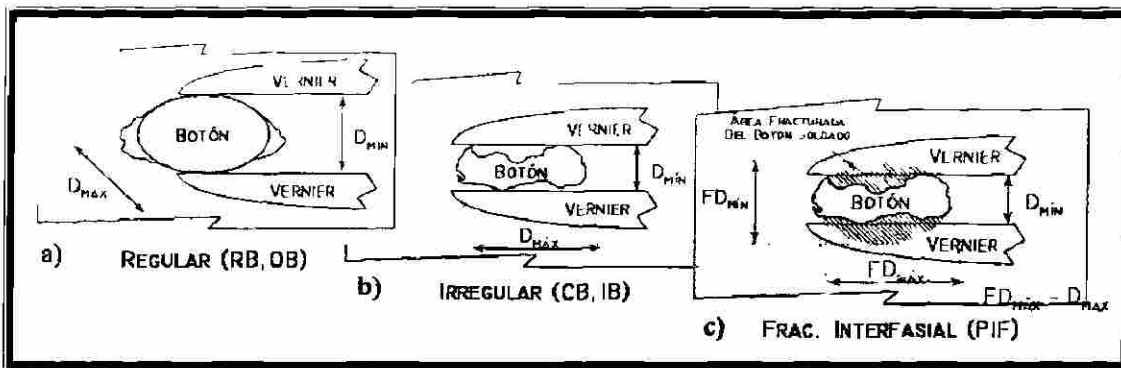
Medición del diámetro del botón de soldadura según el tipo de fractura.
